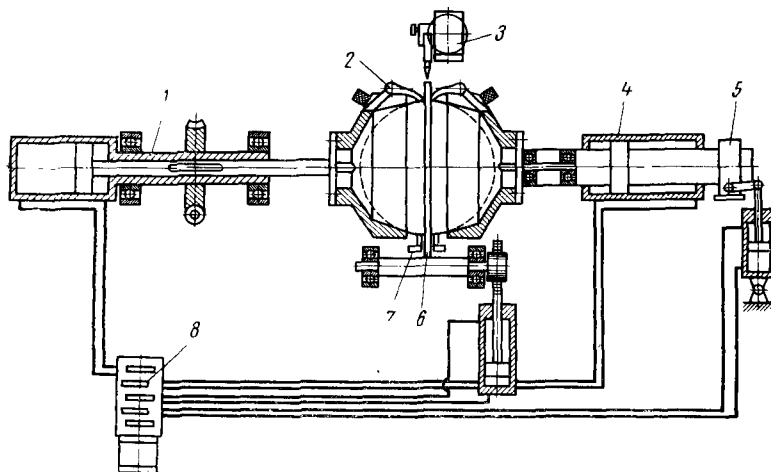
Схема станка-автомата для сборки и сварки пустотелых стальных шаров
